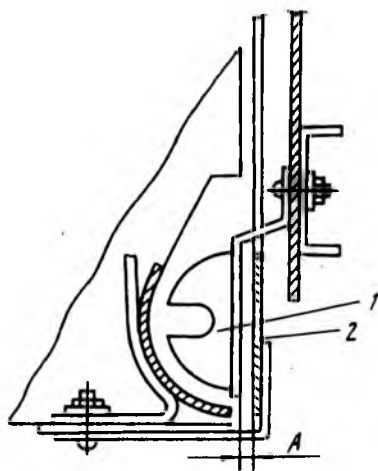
Установка боковой стенки питательного ковша: 1 - ложечка вычерпывающего аппарата; 2 - боковая стенка питательного ковша; А - зазор
